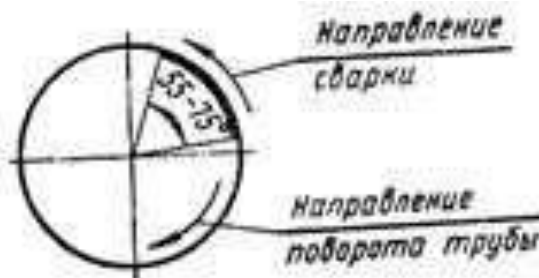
Схема сварки стыка труб малого диаметра
